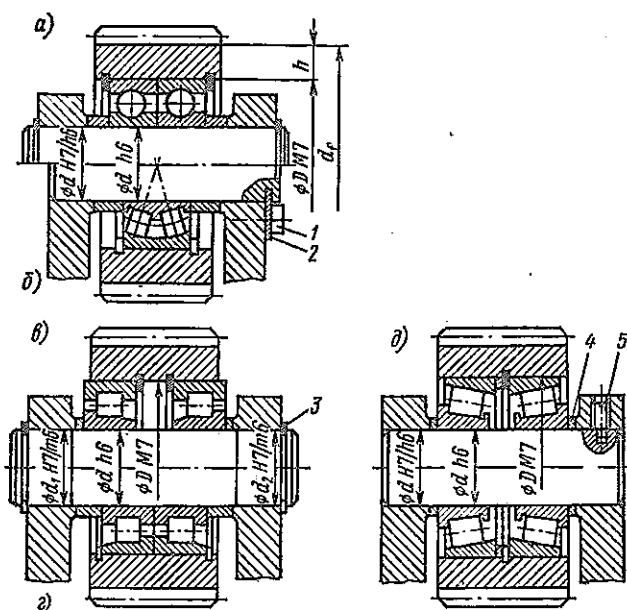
Конструкции узлов сателлитов с подшипниками в отверстиях обода
